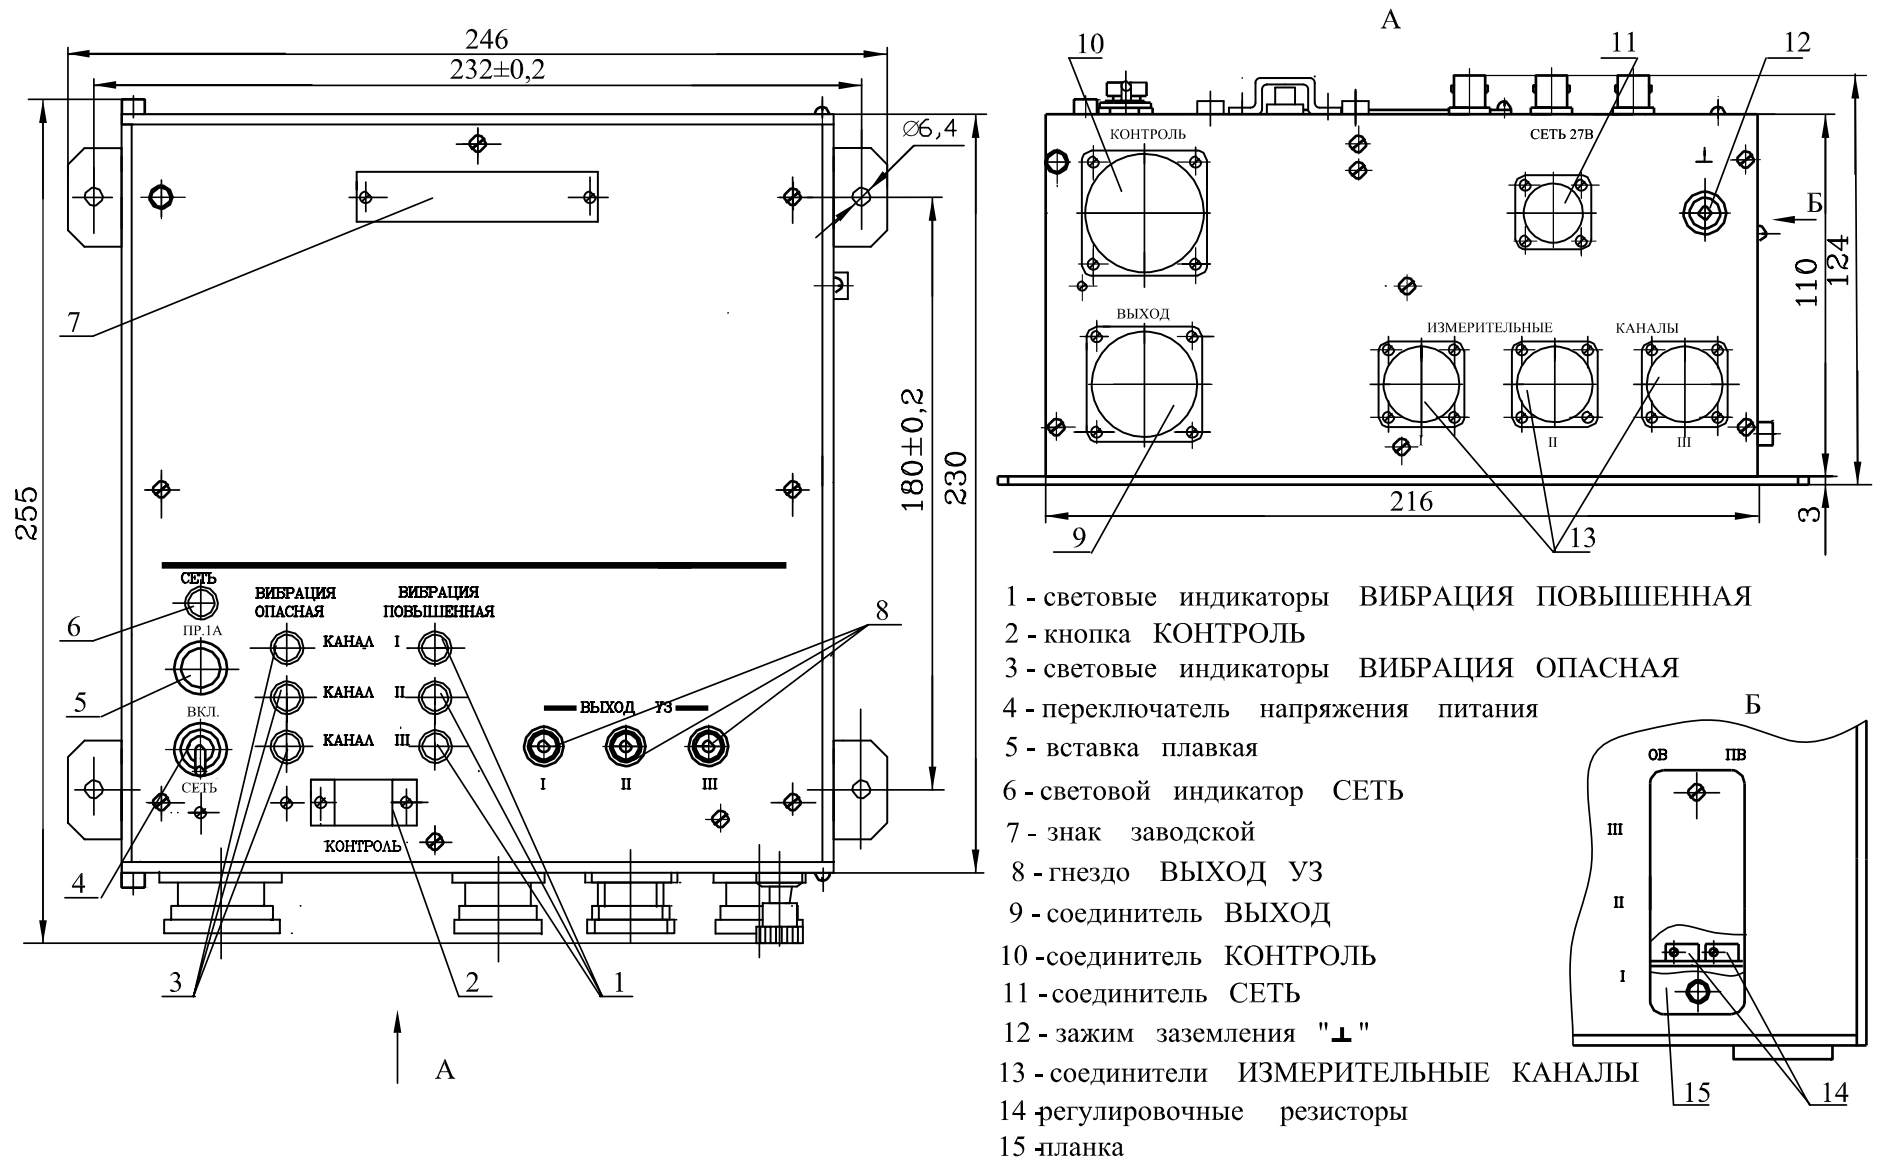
Габаритно-установочные размеры блока БЭ-38-6М.2
